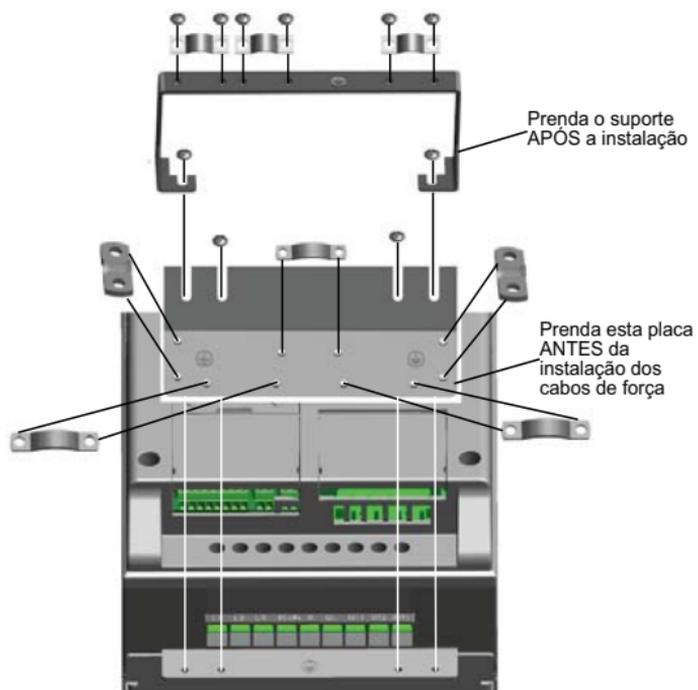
Instalação da placa PE e do suporte a cabo API, MI4 - MI5
